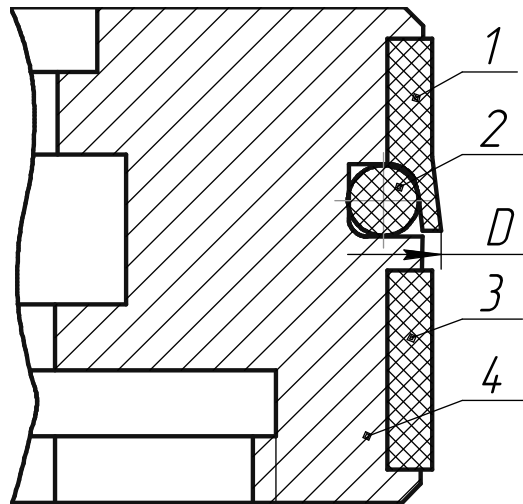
Плавающий поршень гидропневматического устройства: 1 – уплотнительный элемент; 2 – резиновый эспандер; 3 – направляющая втулка; 4 – корпус поршня
